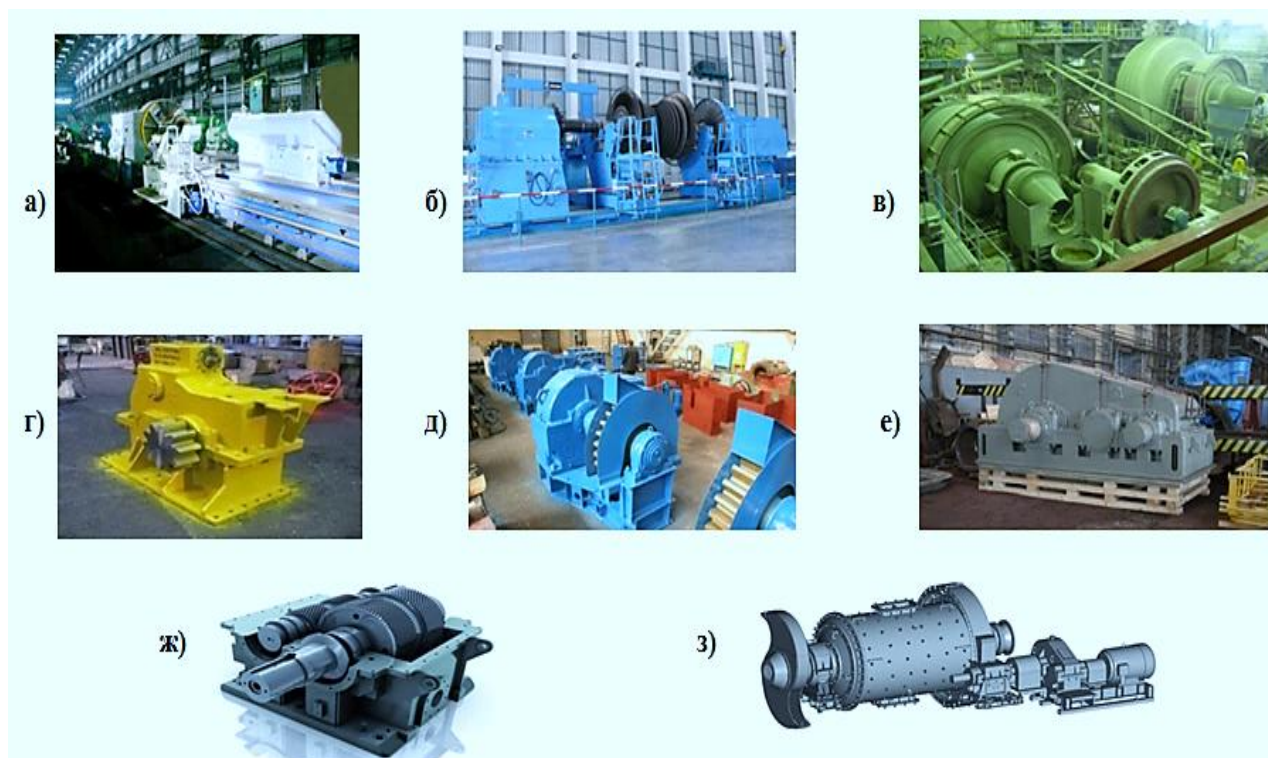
Виды крупномодульных закаленных зубчатых передач тяжелых токарных станков с цилиндрическими колесами:
